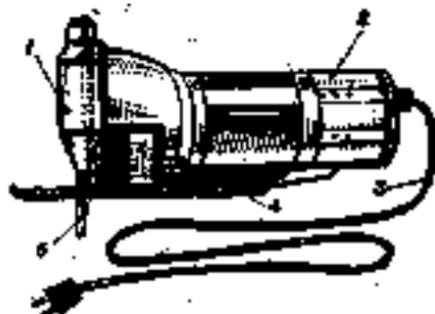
Лобзик электрический: 1 — ручка; 2 — электродвигатель; 3 — выключатель; 4 — корпус для держания пилы; 5 — пила; 6 — резательная головка.
